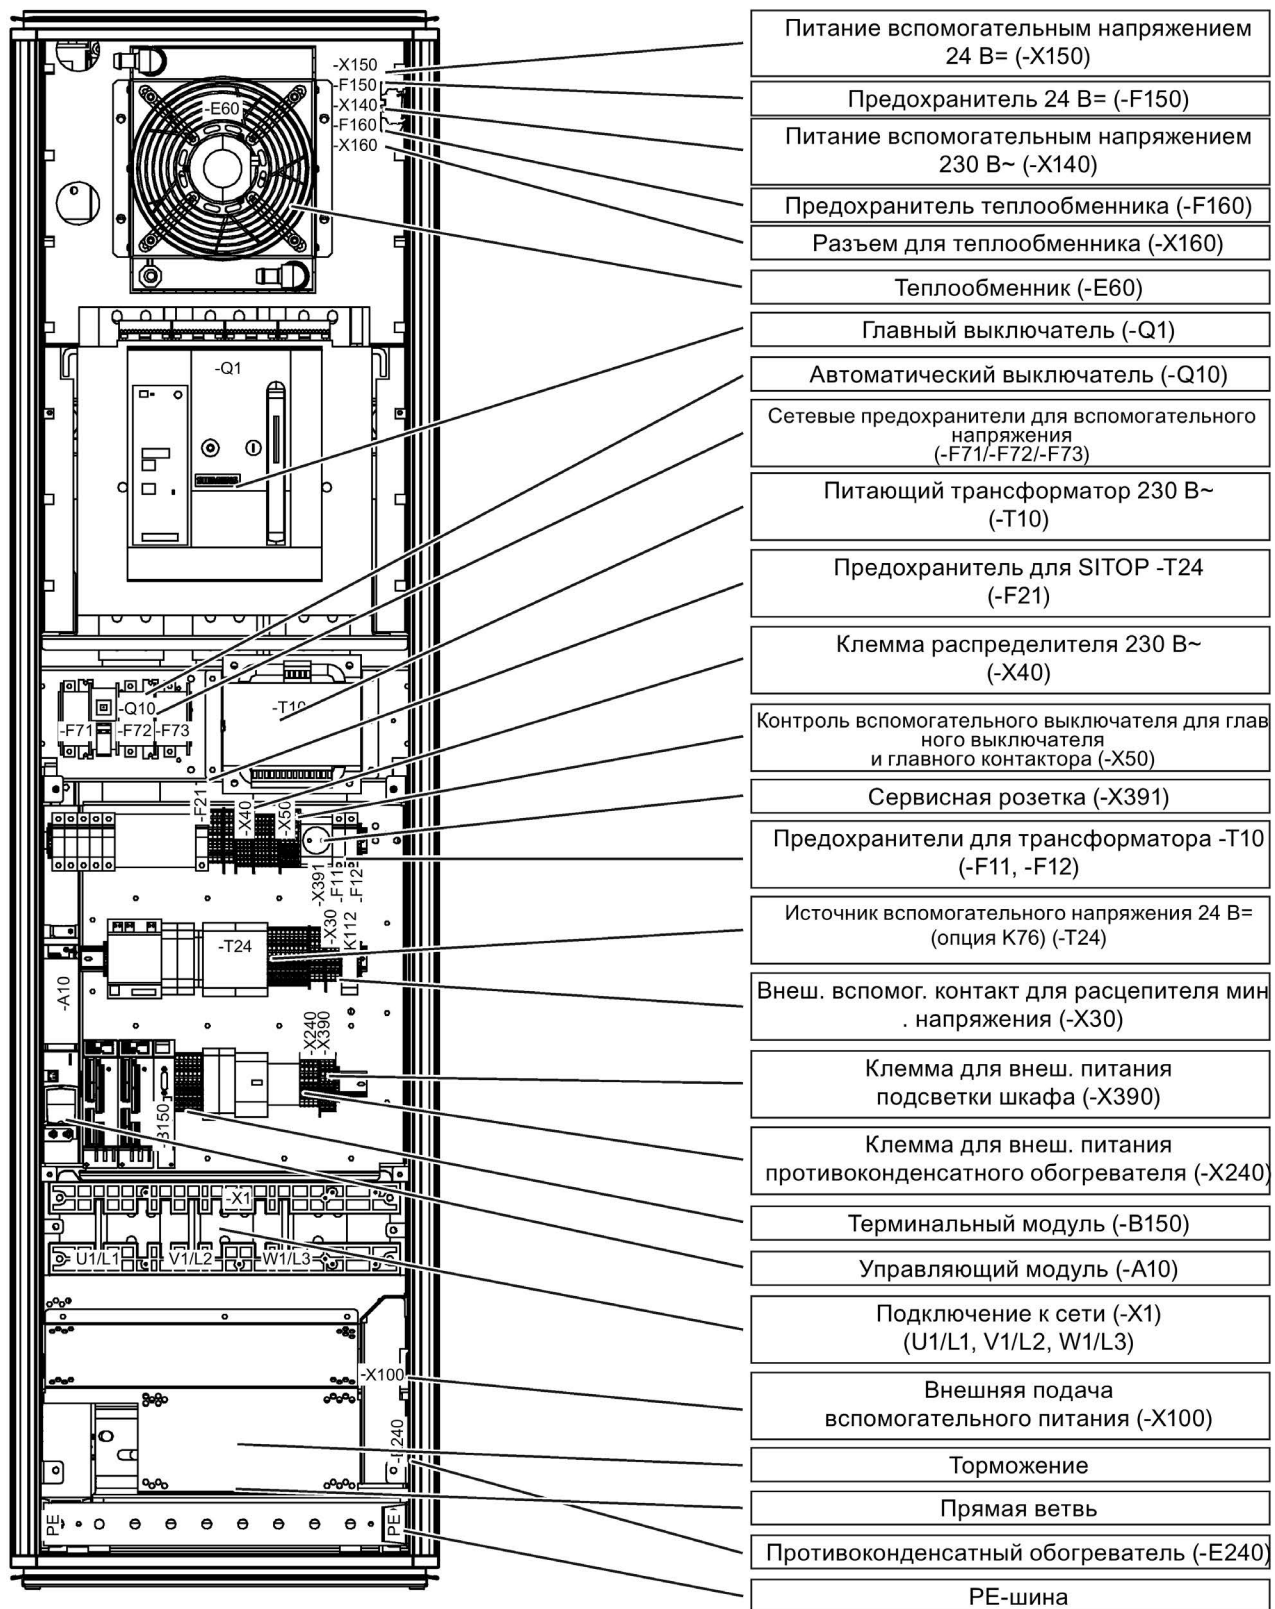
Примеры сборки соединительного активного модуля питания (типоразмер JL)
